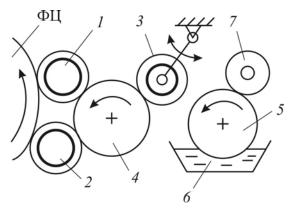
Увлажняющий аппарат контактного типа с прерывистым питанием: 1, 2 — накатные валики; 3 — передаточный валик; 4 — раскатной цилиндр; 5 — дуктор; 6 — корыто; 7 — резиновый ролик; $\Phi \coprod - \varphi$ формный цилиндр
